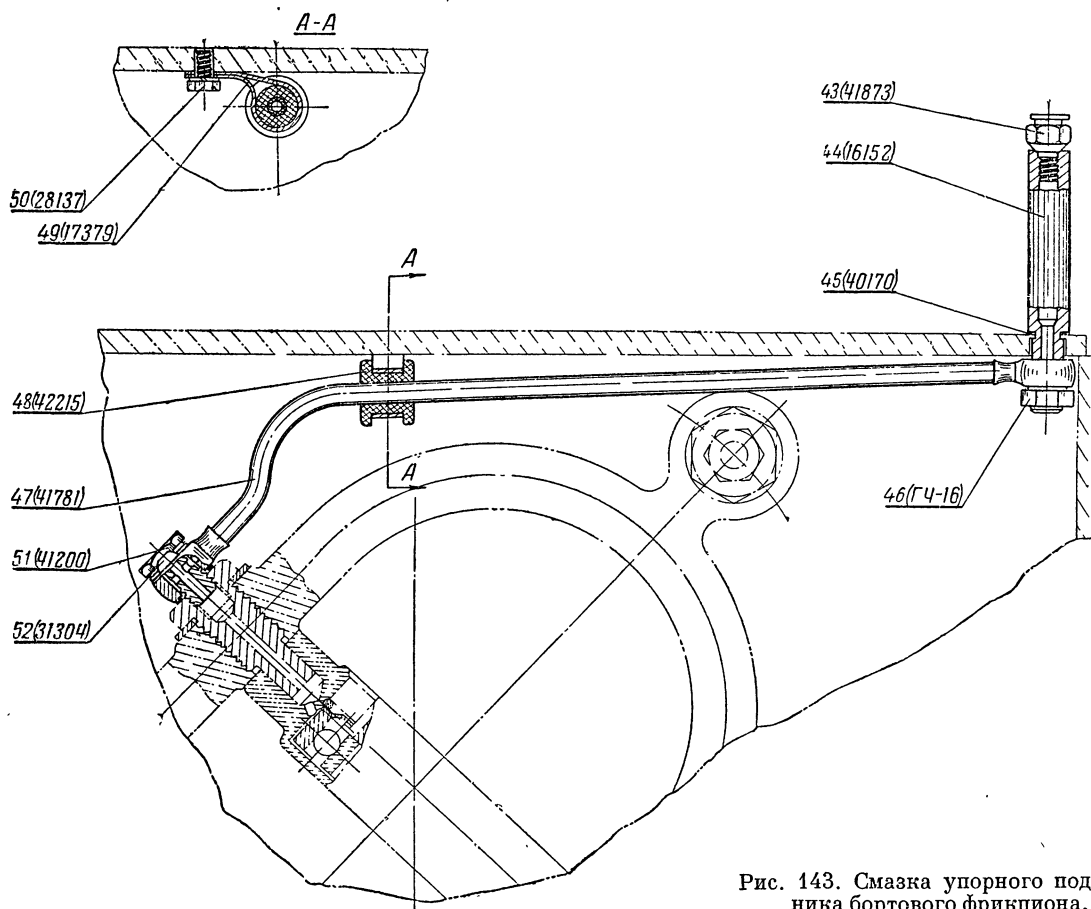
Смазка упорного подшипника бортового фрикциона.
